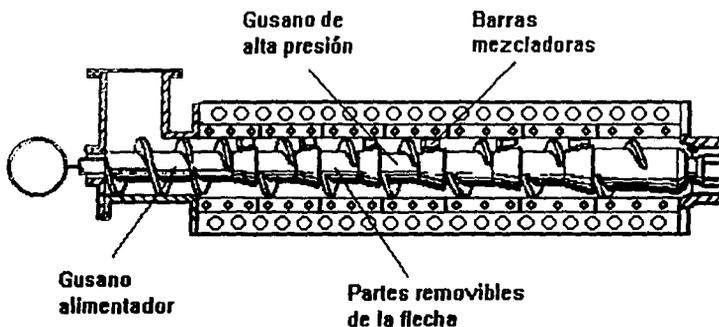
Prensa de tornillo de la Cia. The French Oil Mill Machinery.
